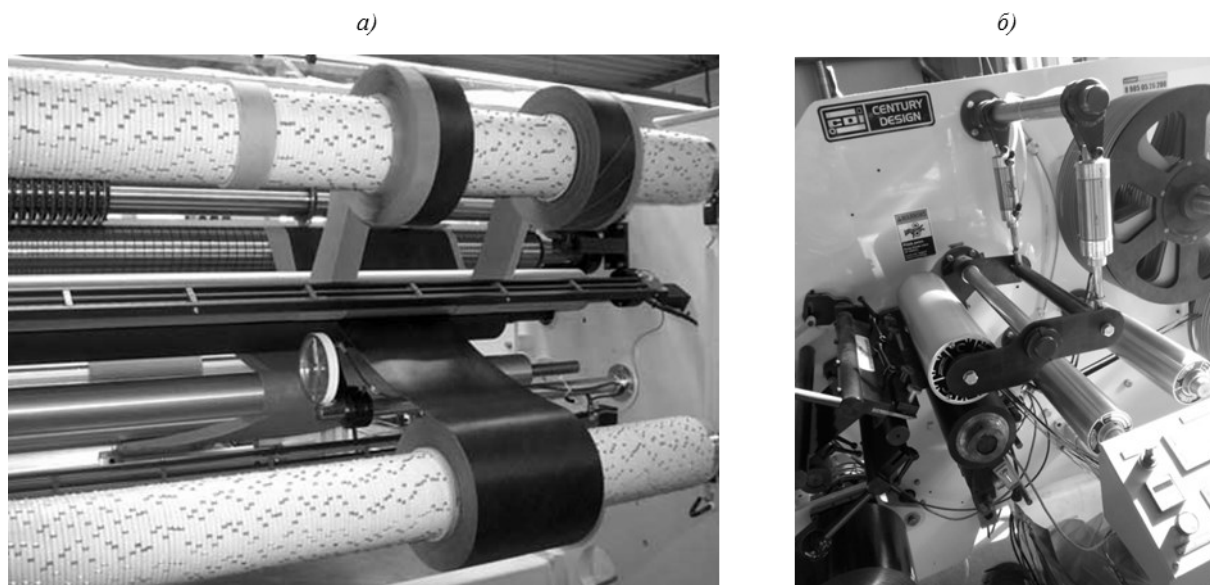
Установка для резки препрегов компаний Robust (а) и CDI (б)
